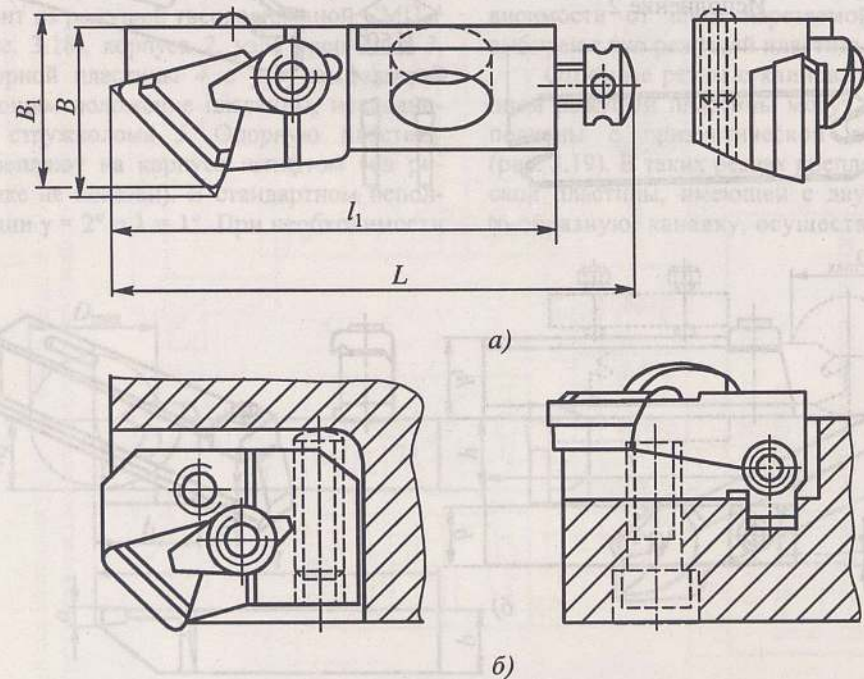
Регулируемый резец-вставка: а – с винтами осевого и радиального регулирования; б – малогабаритный
